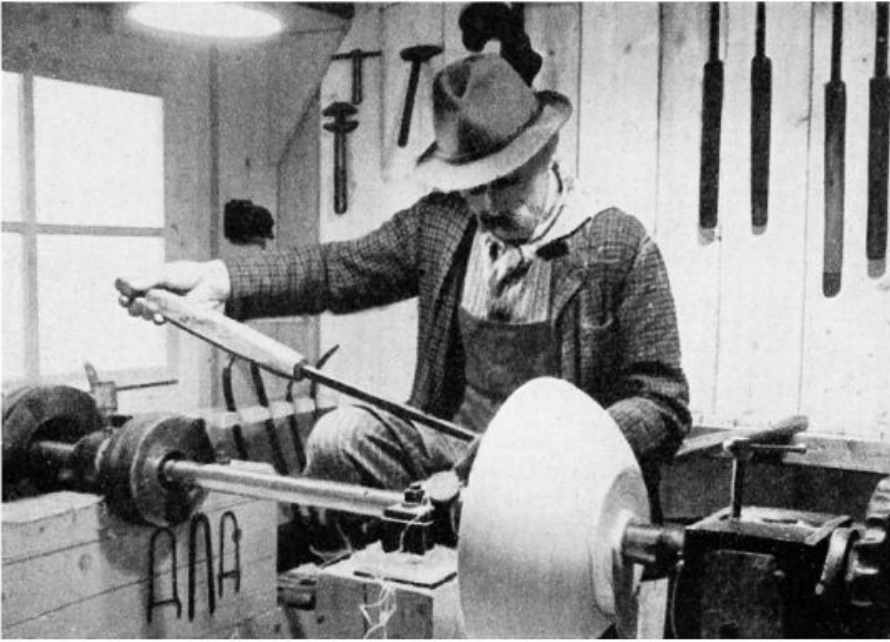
Zwischen 2 starken Spindeln ist das Werkstück auf 2 kräftigen Vierzackspitzen aufgeschlagen (siehe auch Abb. 348 und 349). Die Kraftübertragung auf die Welle geschieht direkt. Um leichter mit starkem Druck das Werkzeug führen zu können, ist gegen Ende des Heftes ein Stück so eingedübelt, daß der Meister den unteren Ballen seiner Hand andrücken kann.
